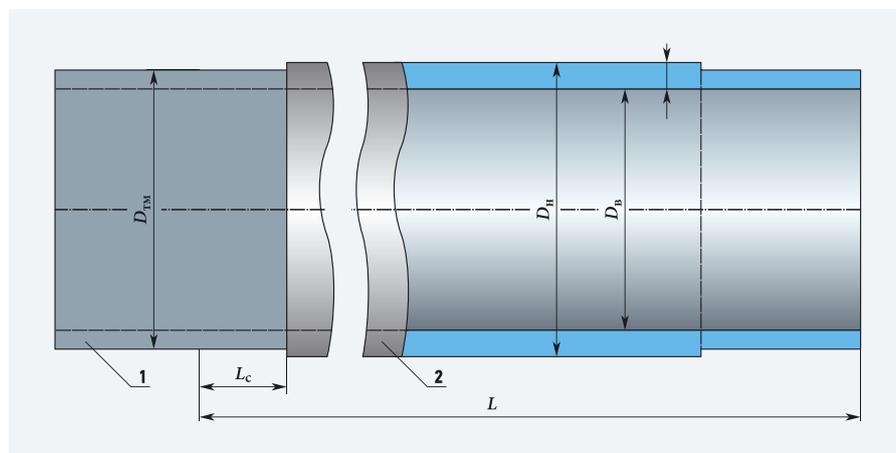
ТРАСВ под муфтовое соединение [1 и 2 — калиброванная часть* и тело трубы; D_n , D_b , t и L — наружный и внутренний диаметры; толщина стенки и длина (3, 6, 9, 12 и 18 м \pm 0,060 м) трубы; $D_{тм}$ и L_c — диаметр и длина калиброванной части трубы; * Часть трубы, обработанная механическим фрезерованием и полиэфирной смолой.  Допускается изготовление труб, применяемых в муфтовом соединении, без калиброванной части, и в этом случае диаметр $D_{тм}$ должен совпадать с наружным диаметром трубы D_n (табл. 1)]
